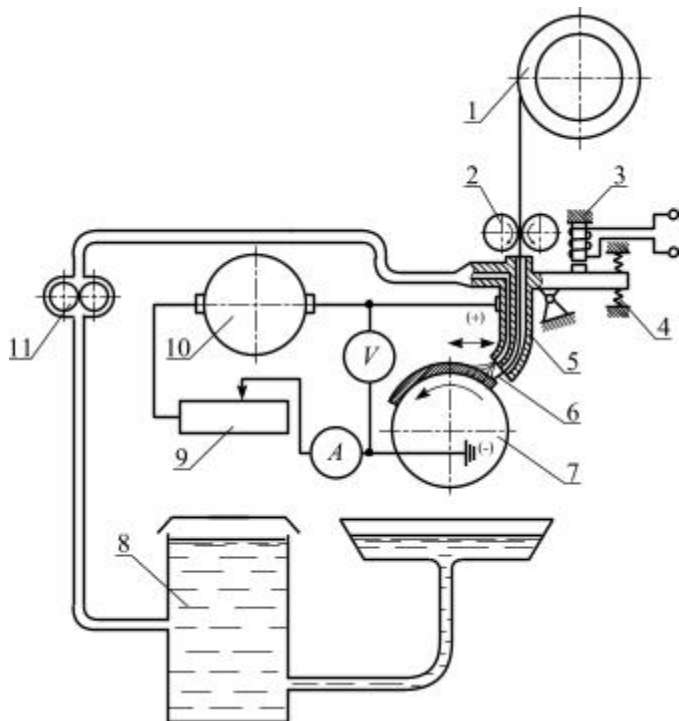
Принципова схема установки для вібродугового наплавлення: 1 – касета; 2 – роликi; 3 – вібратор; 4 – пружини; 5 – мундштук; 6 – електродний дріт; 7 – деталь; 8 – резервуар-відстійник; 9 – дросель; 10 – джерело струму (зварювальний перетворювач); 11 – насос
